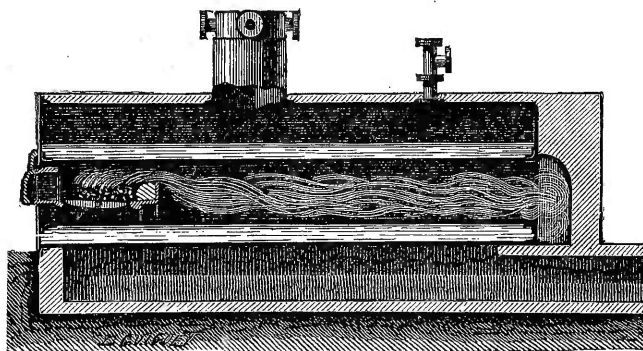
Coupe longitudinale d'une chaudière Cornouailles.
